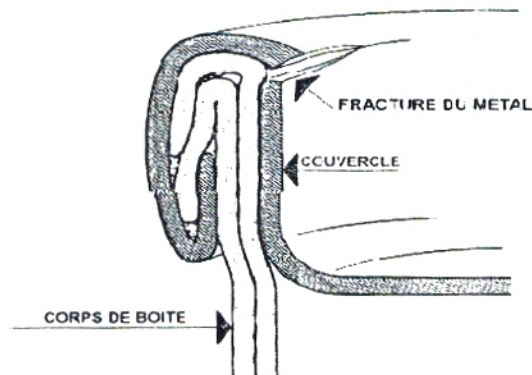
Cut-over sur la soudure longitudinale [8].
